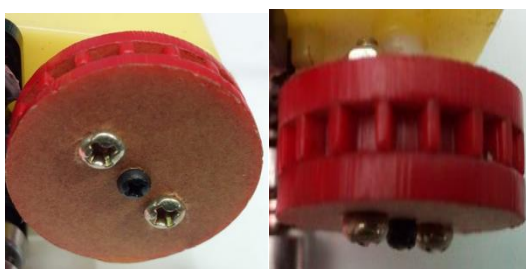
Engranajes entre motor y cadena de transmisión
